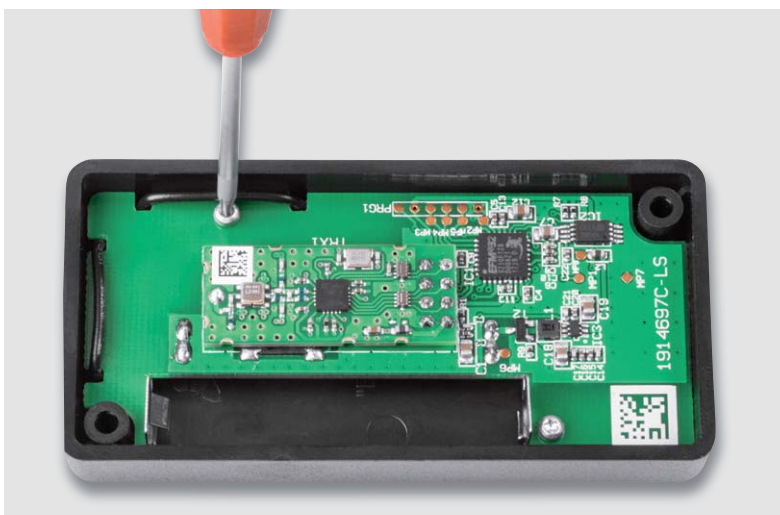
wird mit zwei Schrauben im Gehäuse fixiert.
